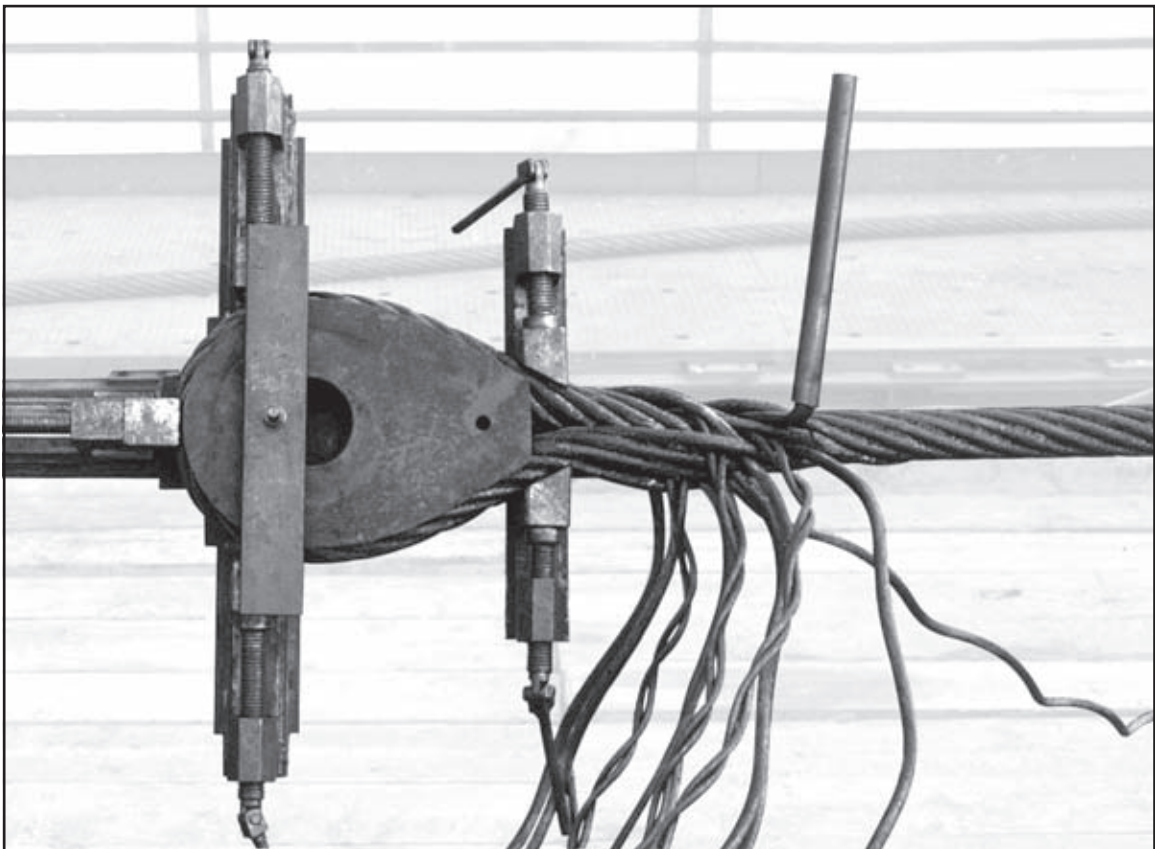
Spleiß an einem achtlitzigen Drahtseil mit Stahleinlage
